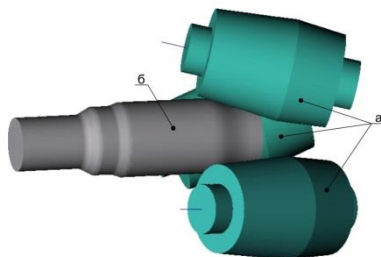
Модель валков (а) и ступенчатой заготовки (б) для расчёта РСП в QFORM-3D
